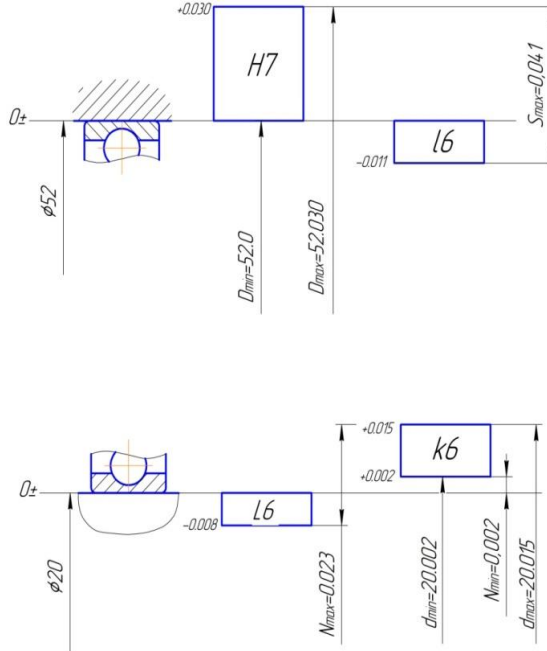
Схема розташування полів допусків підшипникового з'єднання
